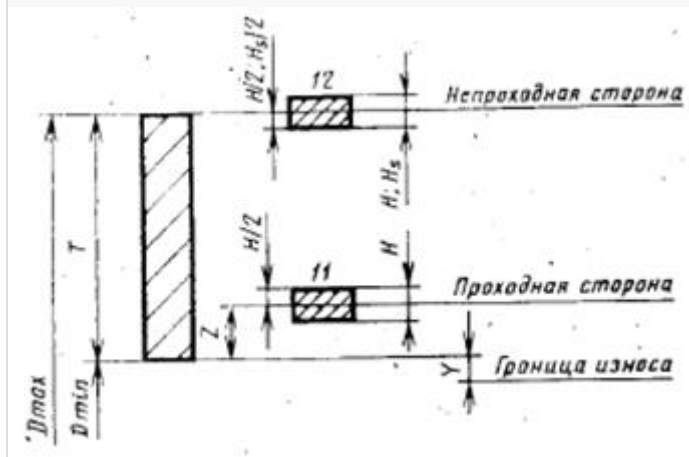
Схема полей допусков калибра-пробки для квалитетов 6-8
